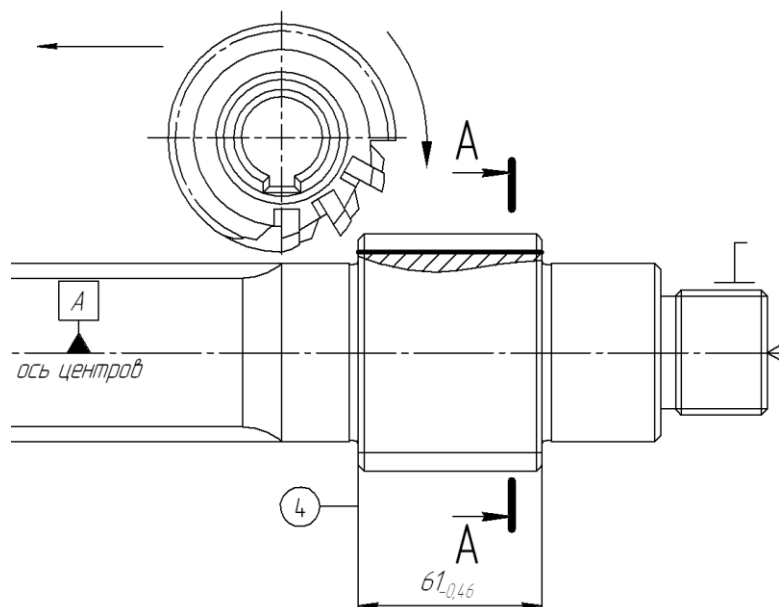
Формоутворення при фрезеруванні дисковою фрезою
